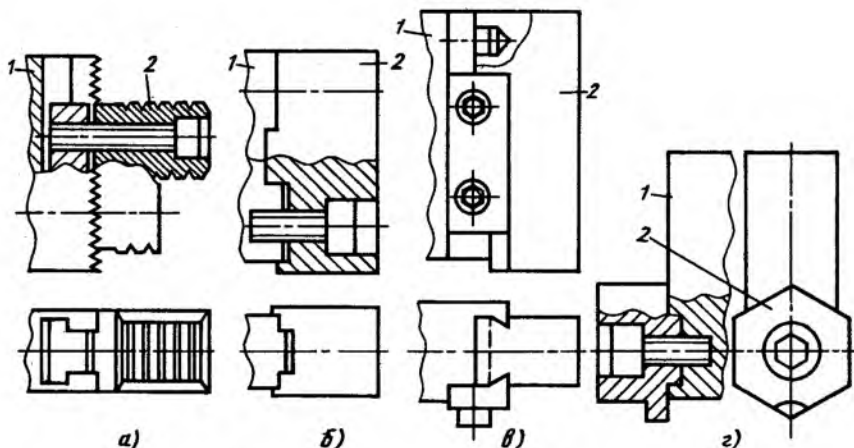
Кулачки самоцентрирующих токарных патронов:
